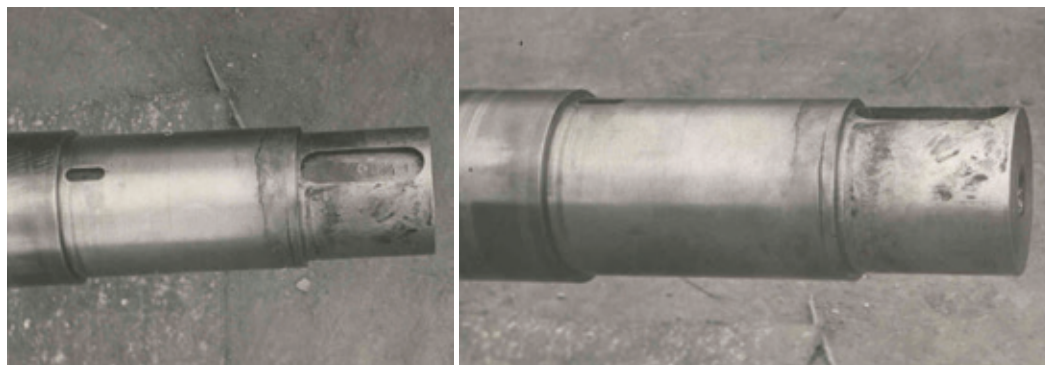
Фреттинг-коррозия на шейке вала ротора компрессора в месте посадки полумуфты (слабая посадка полумуфты — натяг 0,015 мм при допустимом 0,03 мм)
